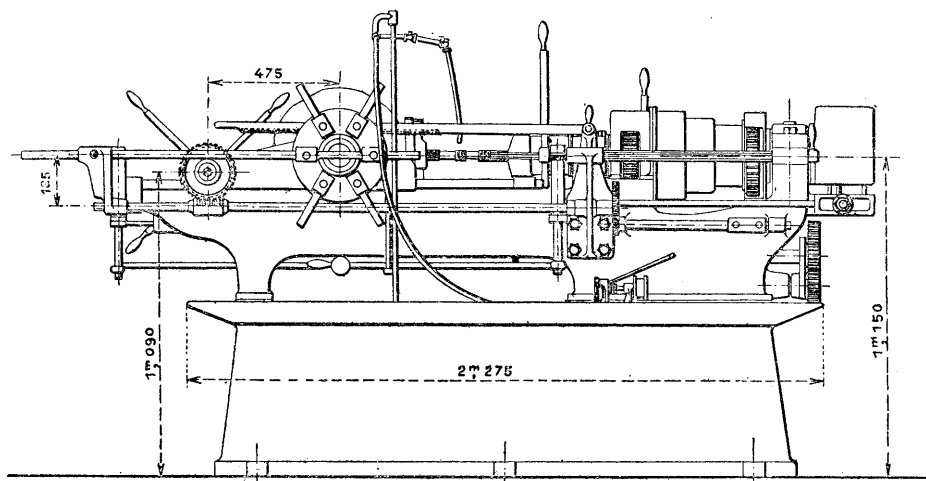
Tour de la Wolseley Sheep Shearing Company, de Birmingham. — Vue d'arrière.
